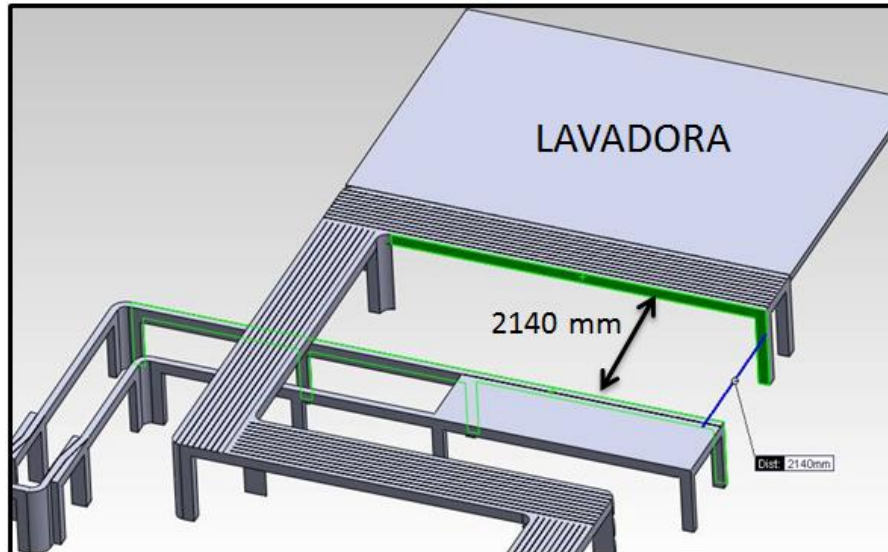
Ubicación del sistema diseñado en la planta de embotellado
